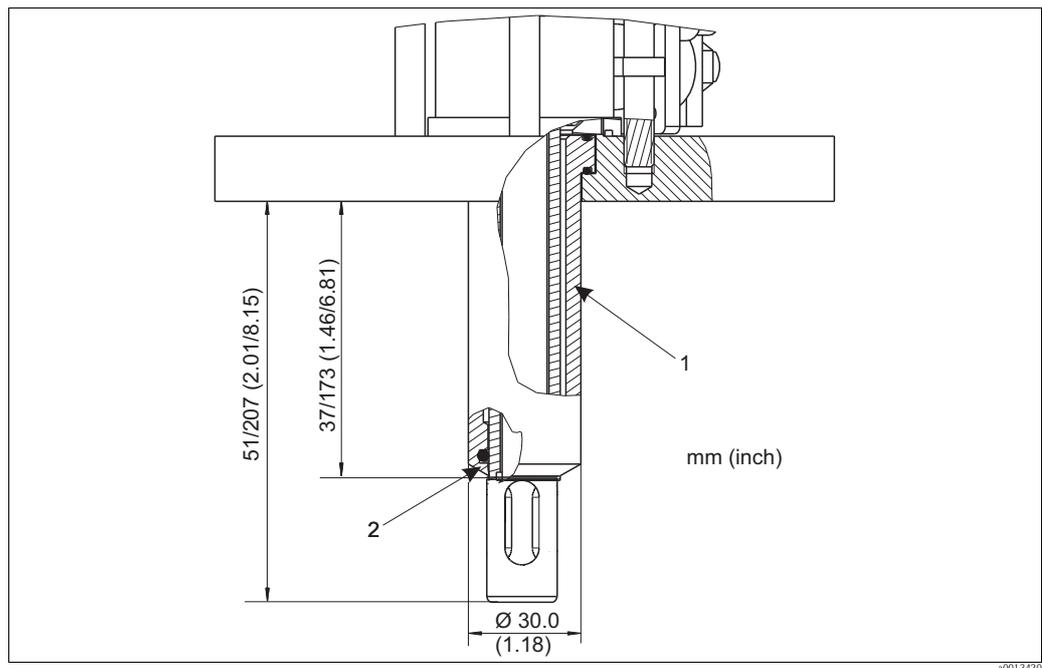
Manchon d'étanchéité (profondeur d'immersion courte/longue)
